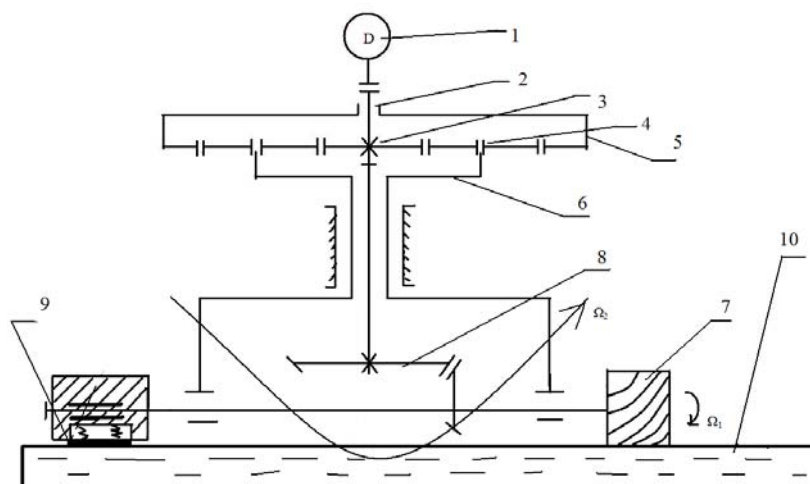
Кинематическая схема привода калибровально-термопротяжного узла:
